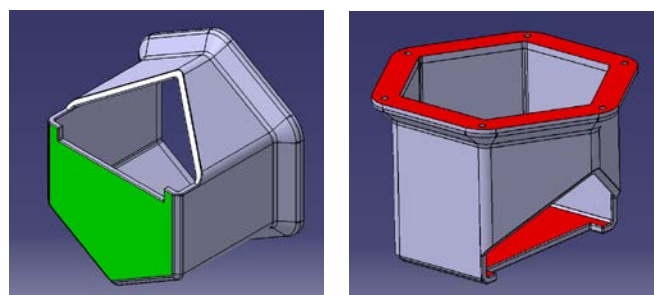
Cara de apoyo durante la impresión. Posición de impresión.
